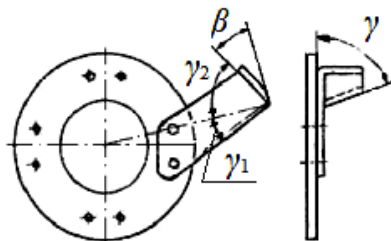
Схема встановлення ножів на фрезерному барабані:
